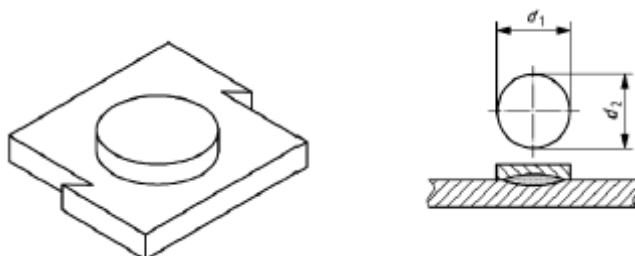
Ponto de Soldadura após Tear Down, Pull out Failure
